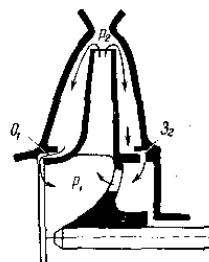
Схема рабочего колеса с двумя уплотнительными кольцами у входа и разгрузочными отверстиями во втулке.
